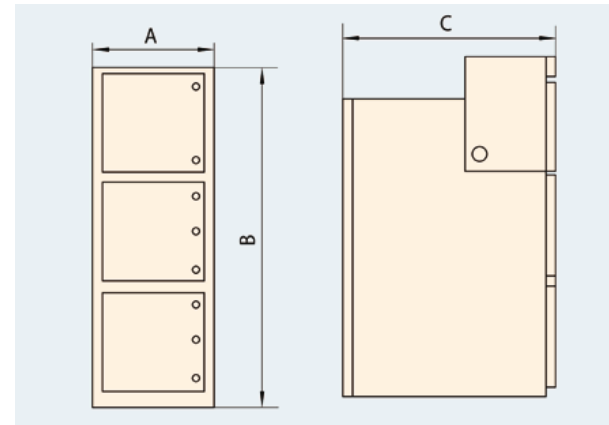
Внешний вид KYN28A-12(Z)(GZS1)
